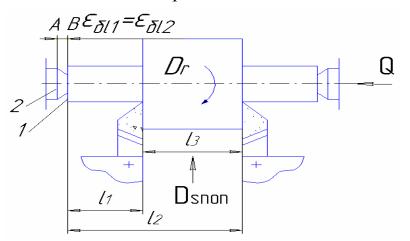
Схема установки заготовки в центра, поясняющая возникновение погрешности базирования
